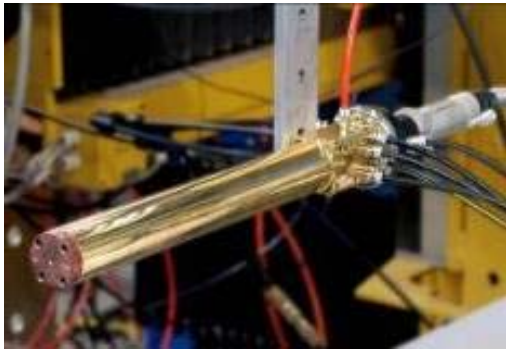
Innenbearbeitungsoptik iClad mit feststehendem Bearbeitungskopf.
